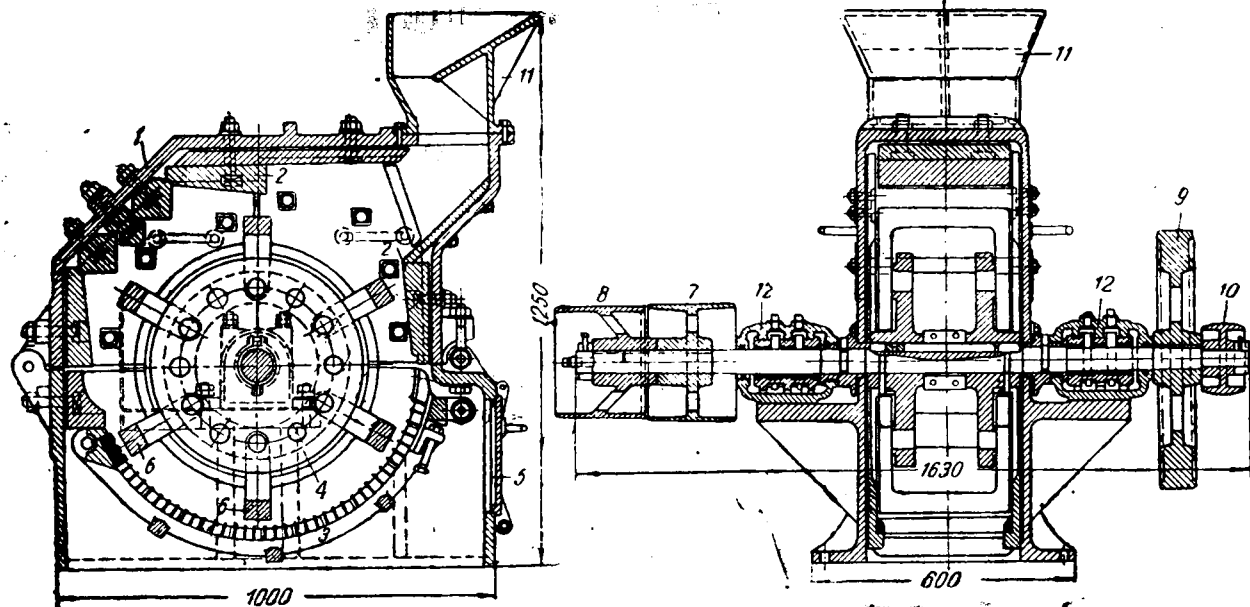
Схема дробилки „Клеро“: 1—корпус, 2—броневые плиты, 3—колосники, 4—диск-билодержатель, 5—смотровой люк, 6—молотки (била), 7, 8 и 9—шкивы, 10—подшипник, 11—питательный бункер, 12—закрытые подшипники.
